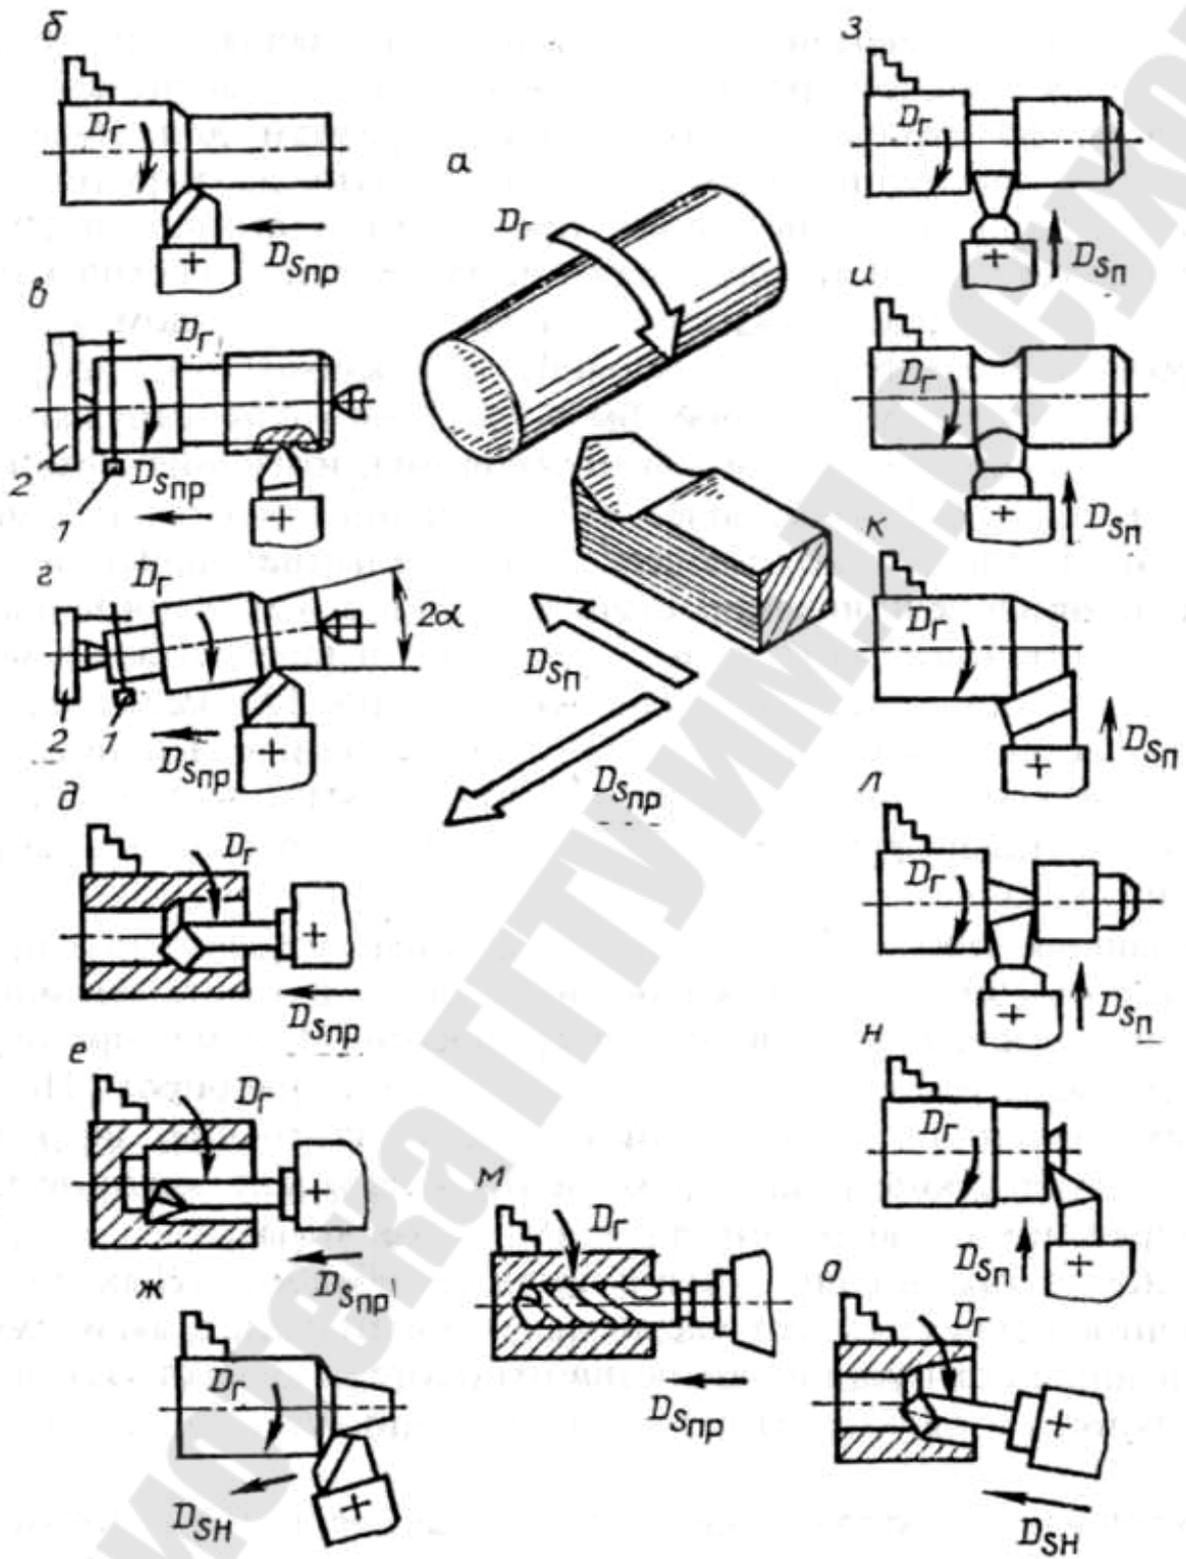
Схемы обработки заготовок на токарных станках
